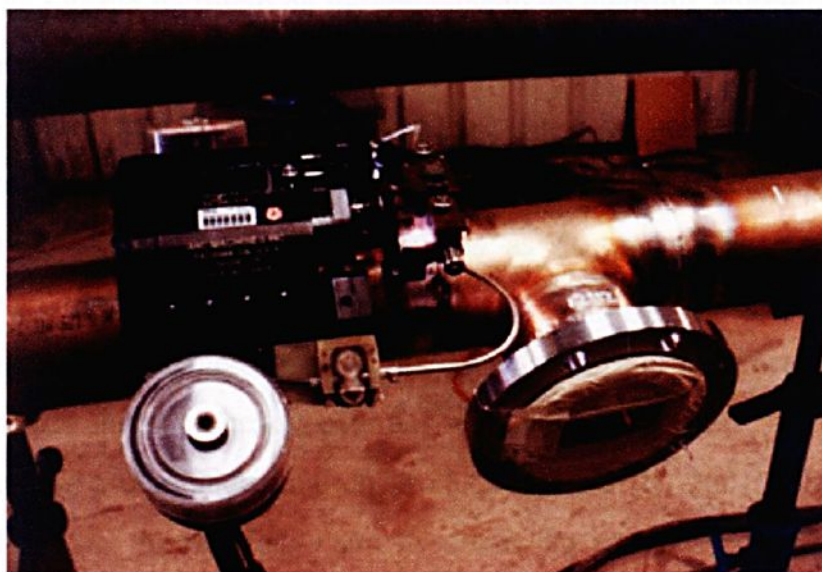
Soldagem de liga Cu-Ni com cabeçote aberto
